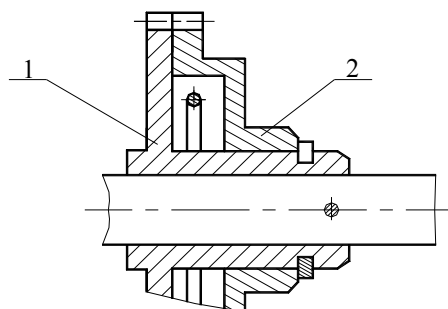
Измените конструкцию таким образом, чтобы уменьшился момент трения между зубчатыми колёсами 1 и 2
